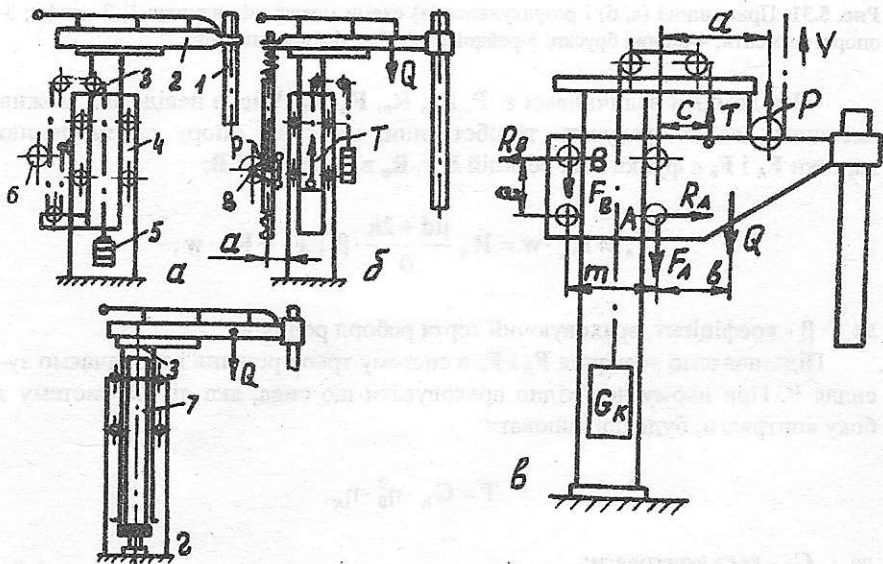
Схеми механізмів переміщення електродів з канатною (а, в) і рейковою (б) передачами, гідравлічного (г): 1-електрод; 2-рукав; 3-рухомий стояк; 4-шхфта; 5-контрвага; 6-лебідка; 7-гідроциліндр; 8-рейкова передача
